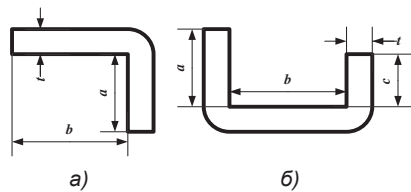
Схема для определения длины заготовки с прямыми внутренними углами: а) угольника, б) скобы
